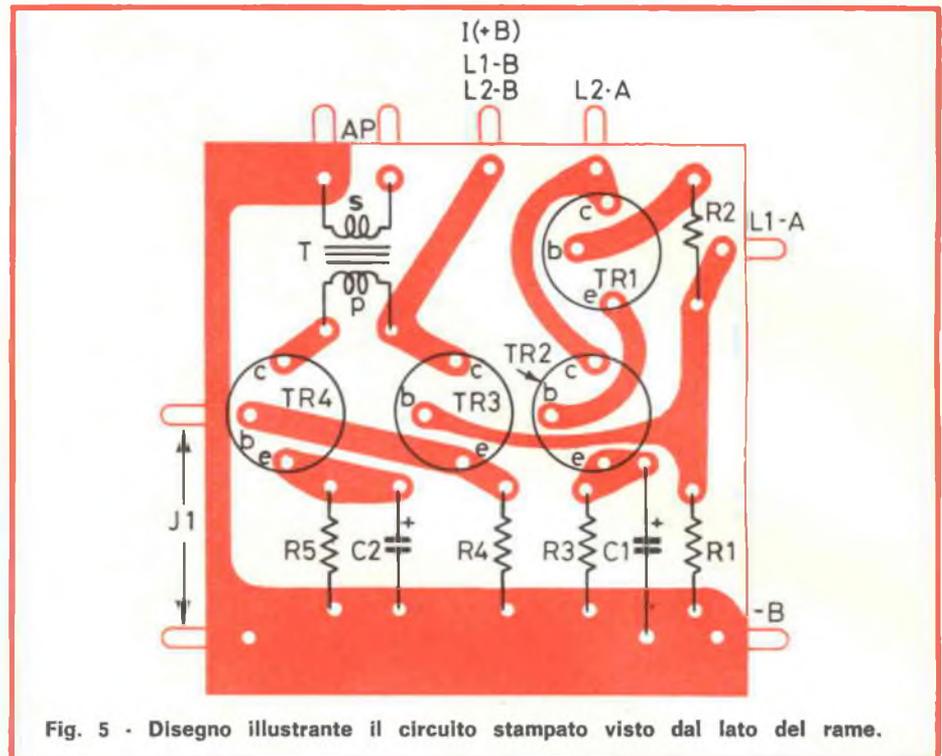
Disegno illustrante il circuito stampato visto dal lato del rame.
